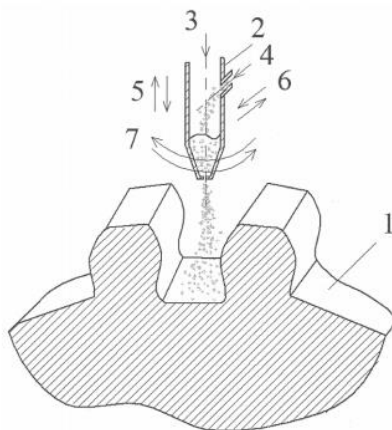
Устройство для упрочнения зубчатых колес шаровой мельницы дробеструйным наклепом
